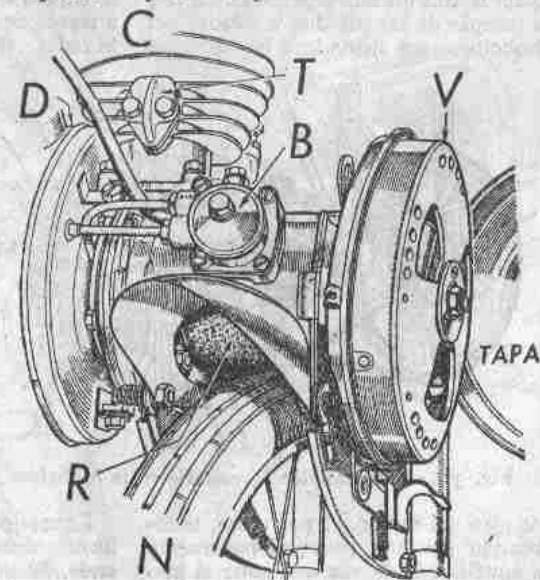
Transmisión del movimiento por rodillo R a la rueda delantera, en el «Velosolex».
